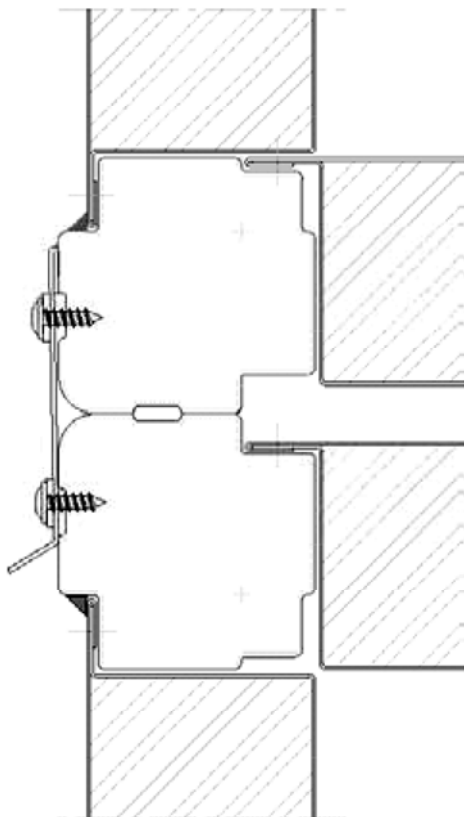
Монтажный профиль и внутреннее расположение агрегата без промежуточной несущей рамы
